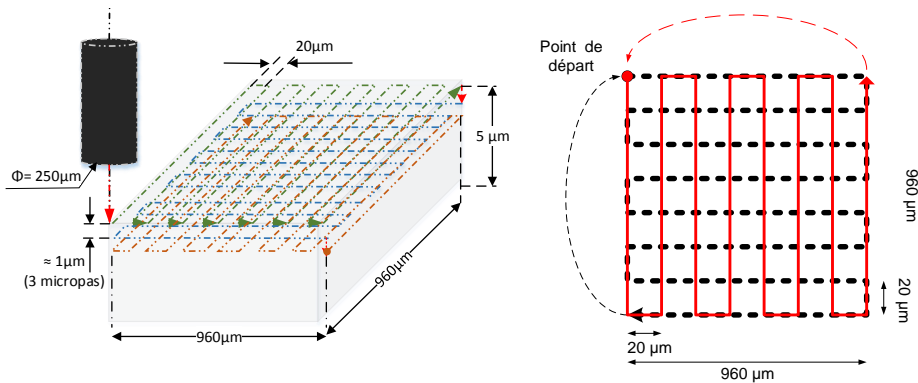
Illustration du parcours d'outil pour l'usinage de la cavité carrée.
